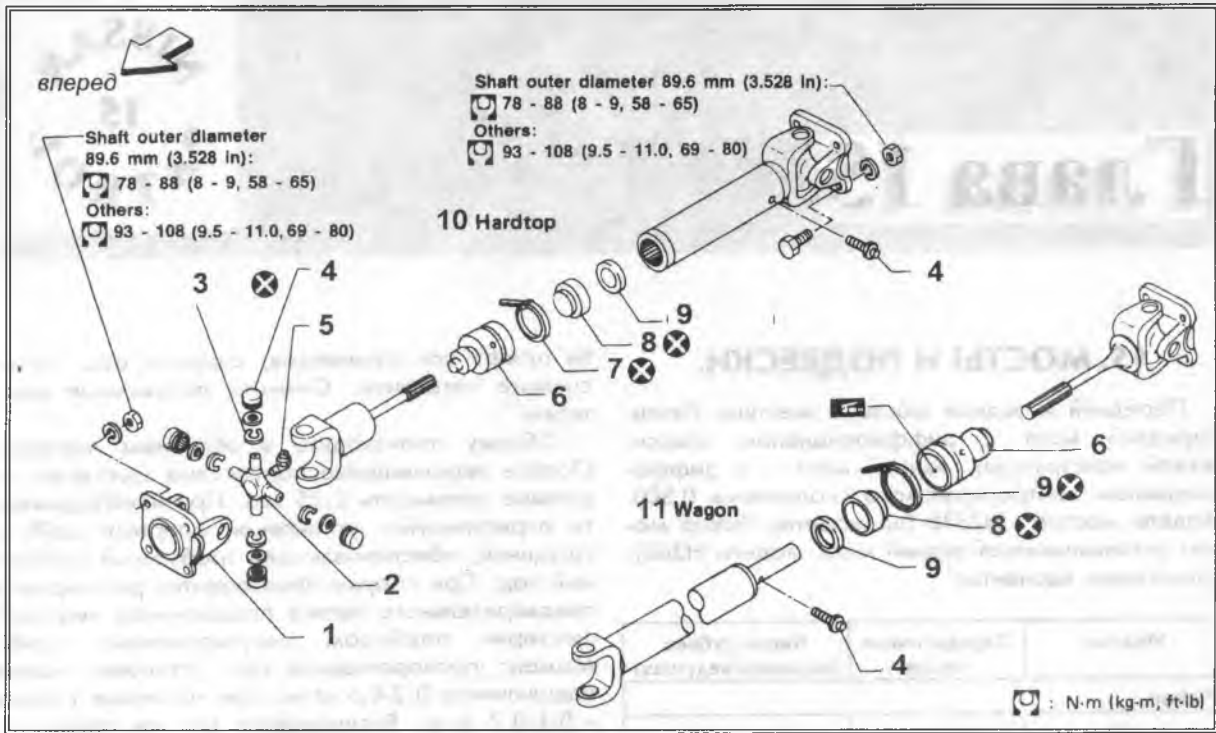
1. Фланец-вилка. Болты крепления фланцев для карданного вала с наружным диаметром 89,6 мм затягивать с моментом 8-9кг-м, для других валов - с моментом 9,5-11 кг-м. 2. Крестовина. 3. Стопорное кольцо. Повторно не использовать. 4. Пресс-масленка. 5. Подшипник. 6. Пылезащитный колпачок. 7. Зажим. 8. Обойма сальника. 9. Сальник. 10. Для моделей с кузовом хардтоп. 11. Для моделей с кузовом фургон.
